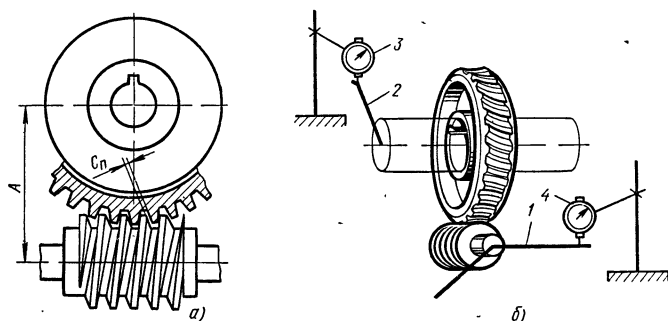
Боковой зазор в червячной передаче (а), схема проверки его индикатором (б)
